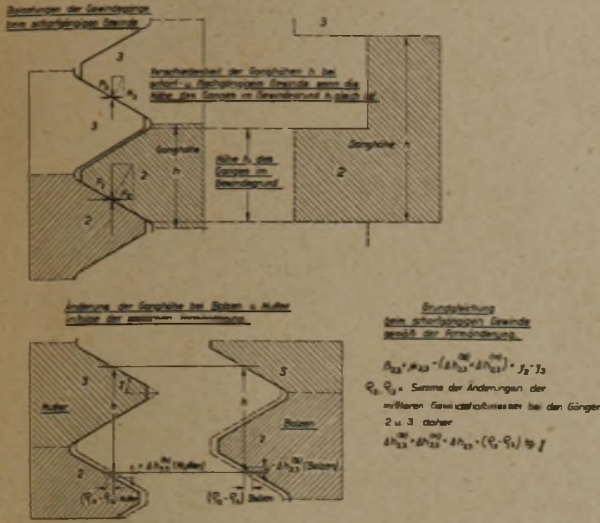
Kräfte im Gewinde, seitliche Formänderung und Grundgleichung beim scharfgängigen Gewinde.
